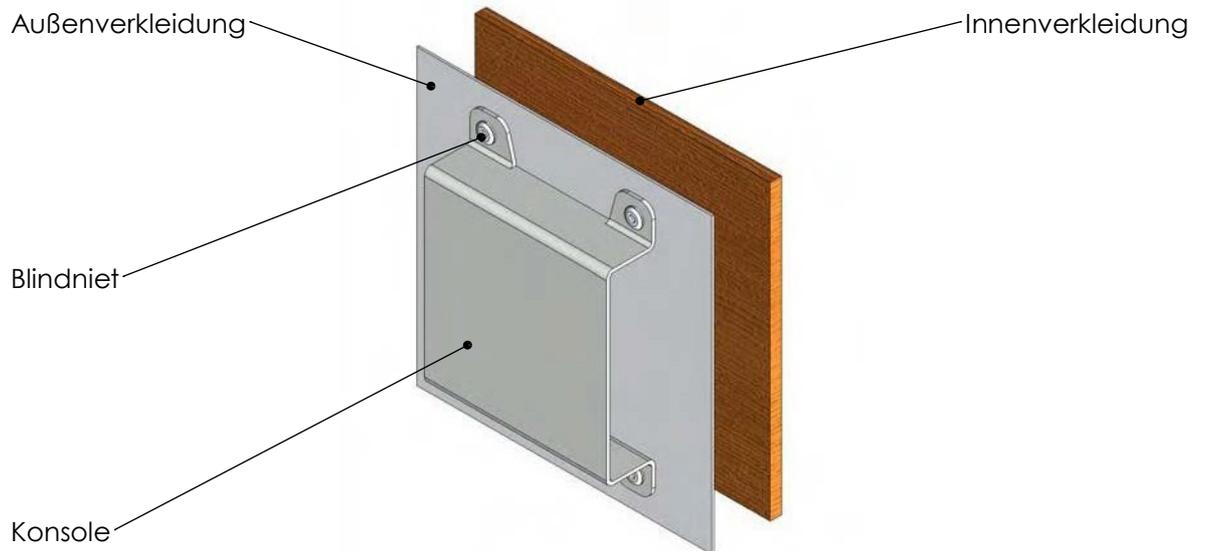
Befestigungsvorschlag für Typenschilder bei Hohlprofilen
